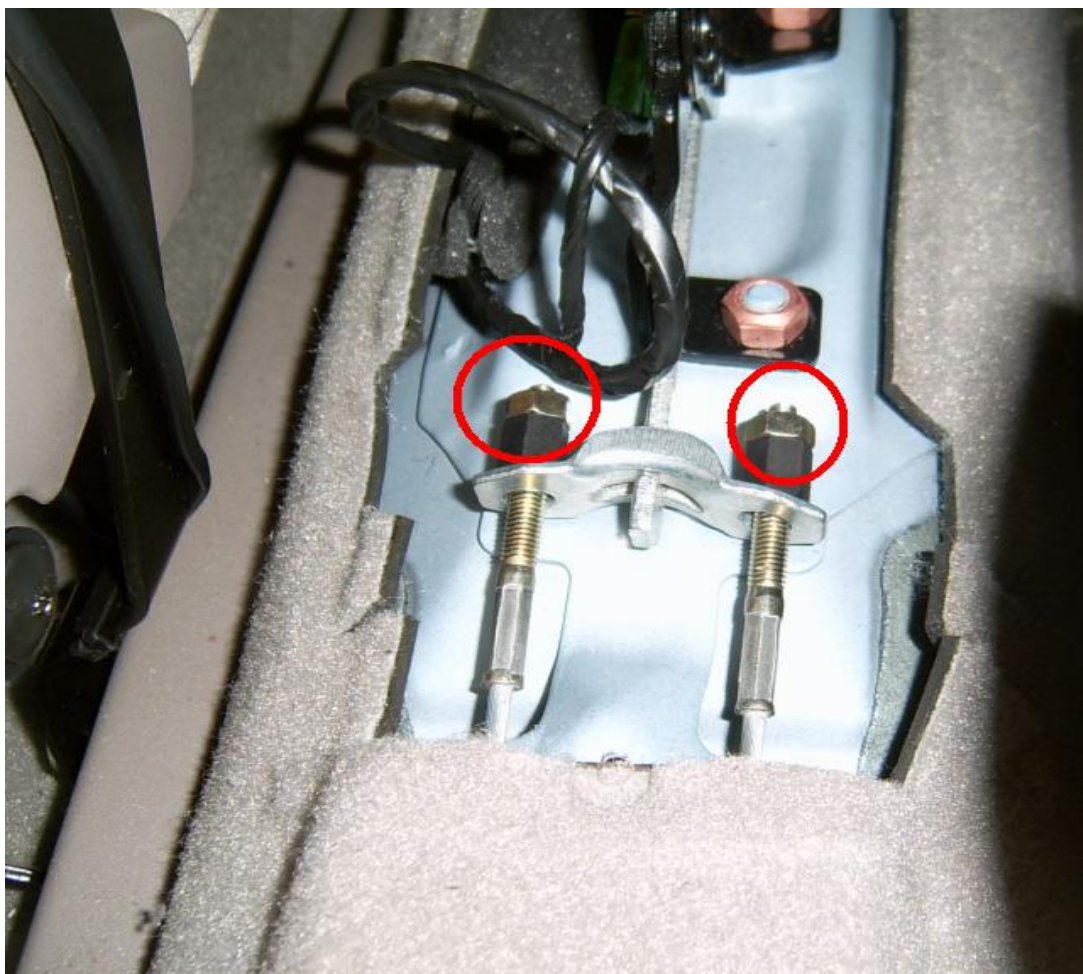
Крепление крышки консоли и стояночный тормоз.
